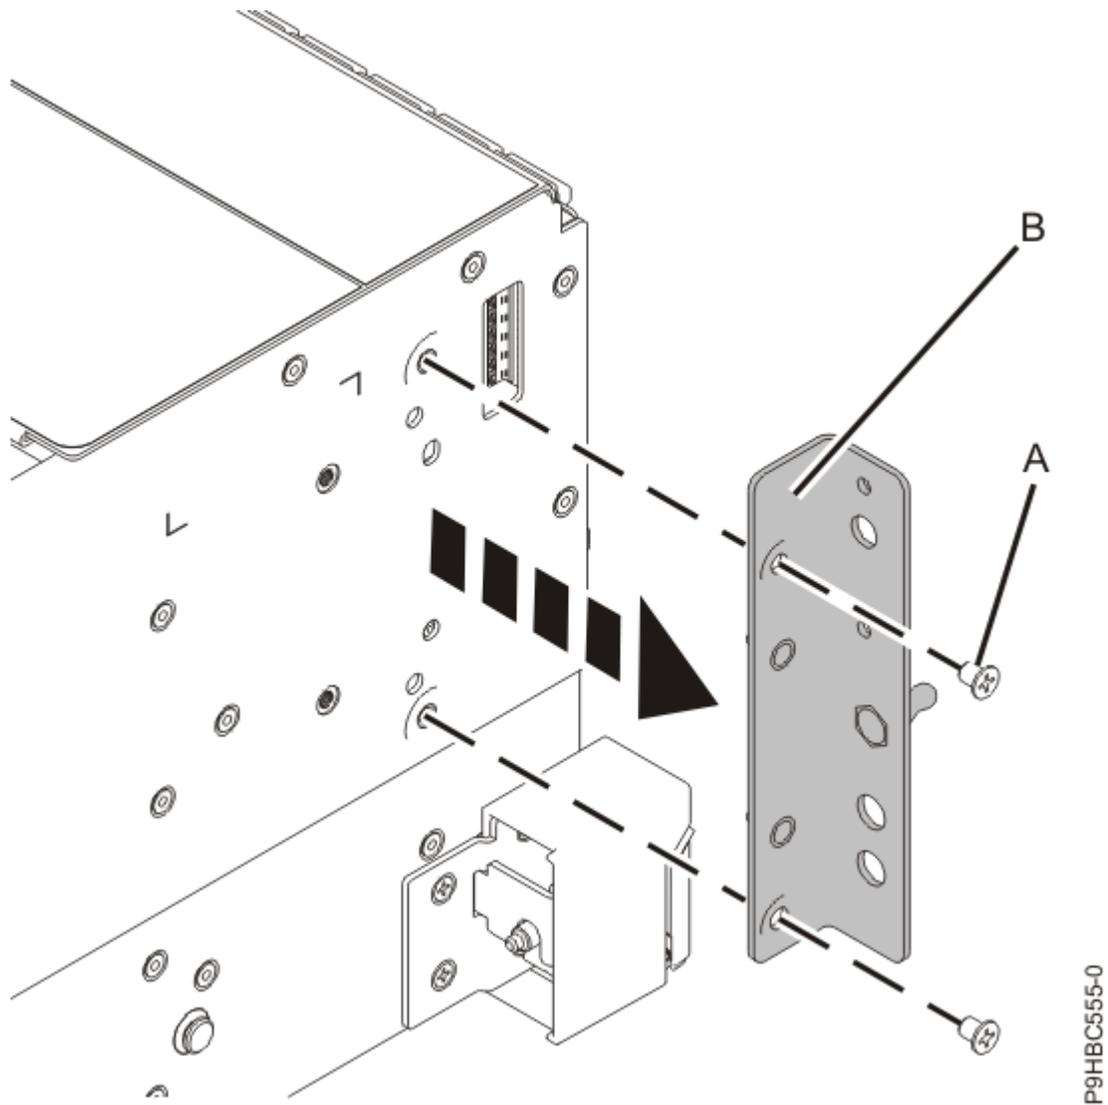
Remover o suporte do painel de controlo de um sistema montado em bastidor
